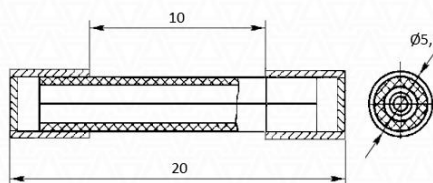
Габаритні розміри запобіжника ZH214-015
